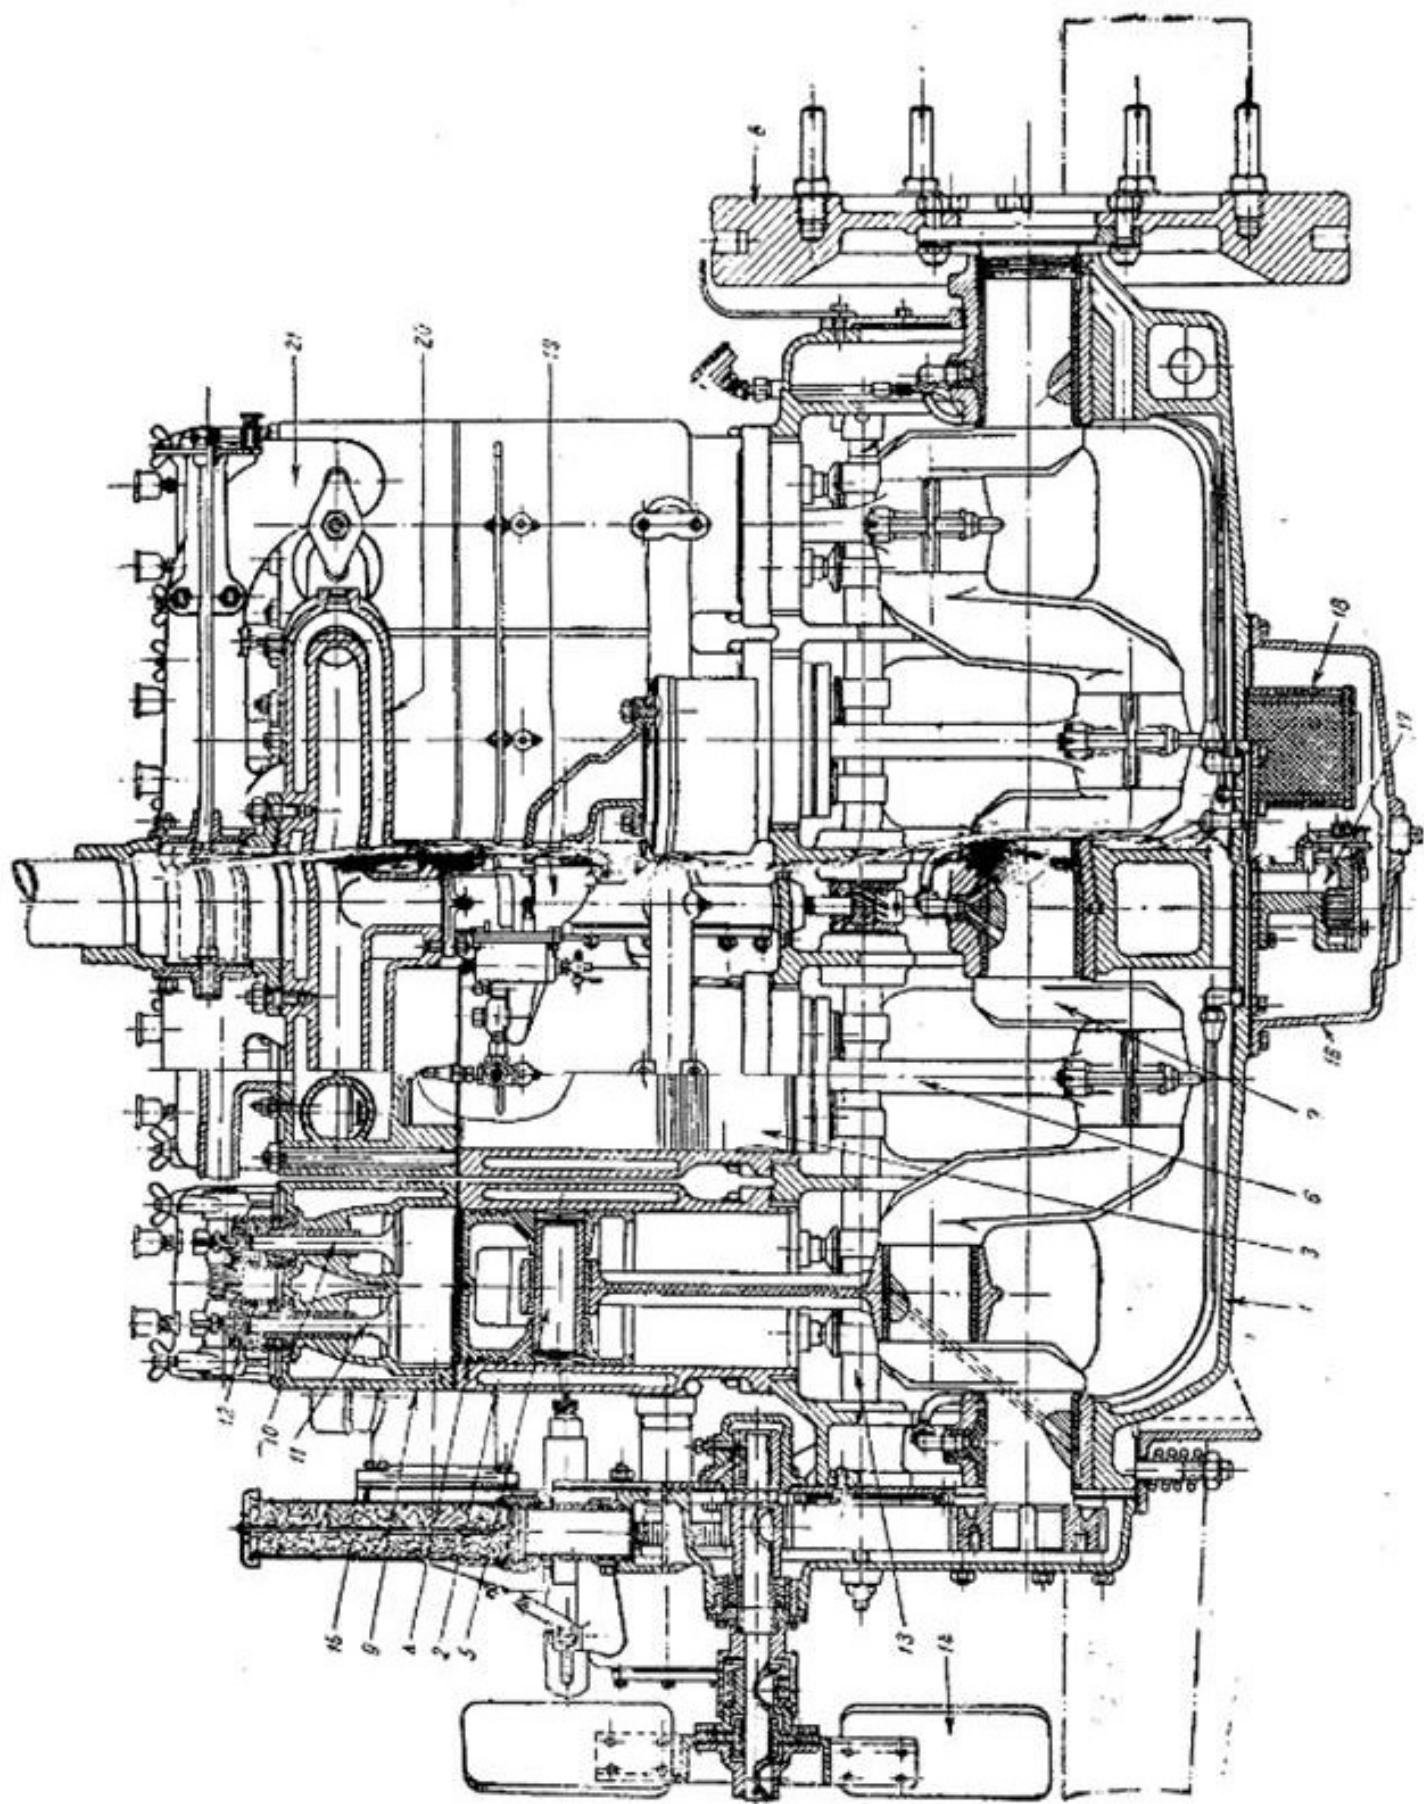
1 — картер; 2 — цилиндр; 3 — поршень; 4 — поршневое кольцо; 5 — поршневый палец; 6 — шатун; 7 — коленчатый вал; 8 — маховик; 9 — головка цилиндра; 10 — всасывающий клапан; 11 — выхлопной клапан; 12 — пружина клапана; 13 — распределительный вал; 14 — вентилятор; 15 — сапун; 16 — поддон; 17 — масляный насос; 18 — масляный фильтр; 19 — карбюратор; 20 — всасывающая труба; 21 — выхлопная труба.
